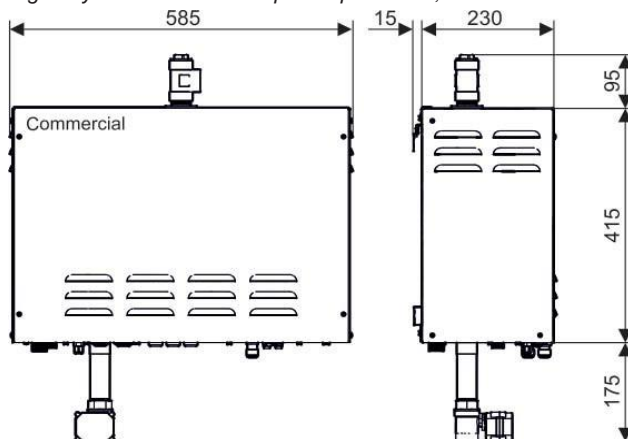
Tylö Generatore di vapore Tipo COMMERCIAL, dimensioni in Millimetri
